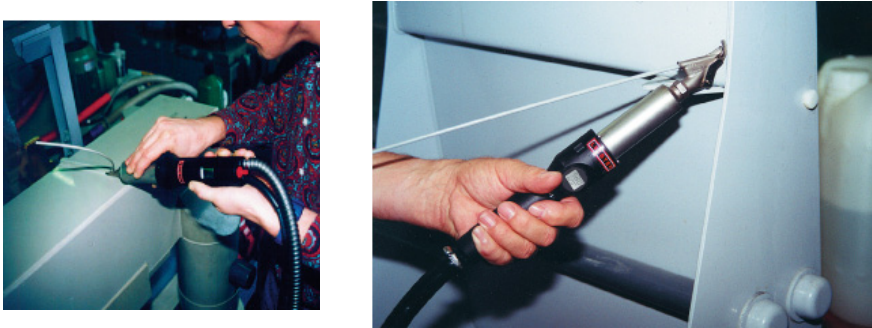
Equipo de soldadura manual con aportación de varilla
